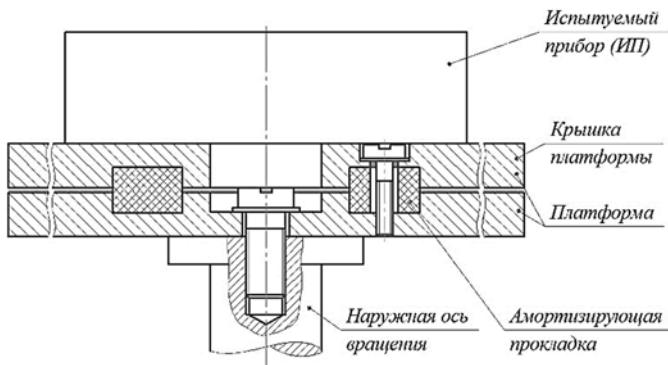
Конструктивная схема амортизирующего узла платформы стенда
